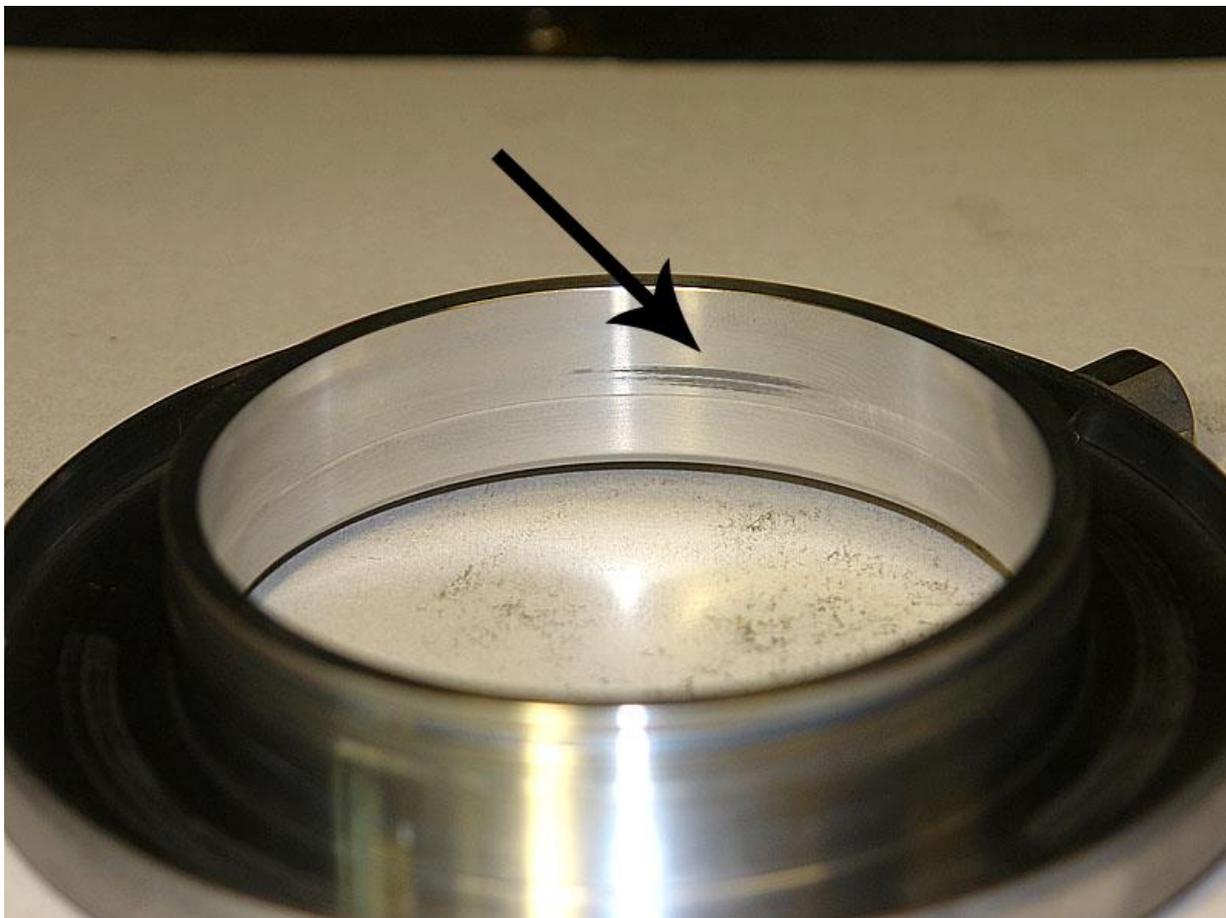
Следы «цепляния» вращающихся деталей планетарного ряда за неподвижный корпус тормоза UD.
